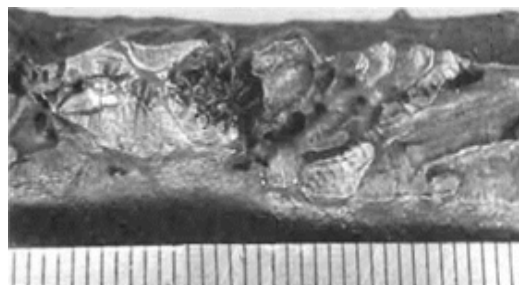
Червячные поры в разрушенном сварном соединении
